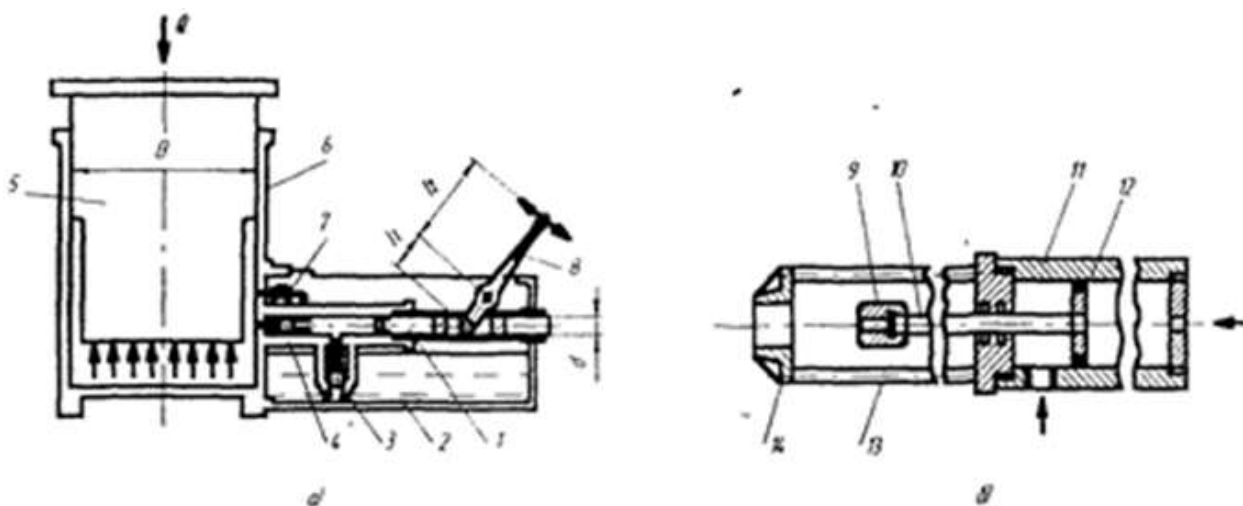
Гидравлический домкрат: а — с ручным приводом; б — тянущий для натяжения стержней
